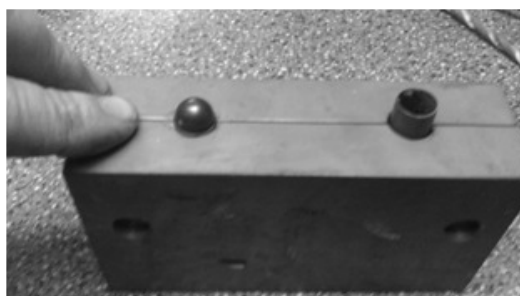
Bomba de una trompeta en molde con bola de acero en un extremo.
